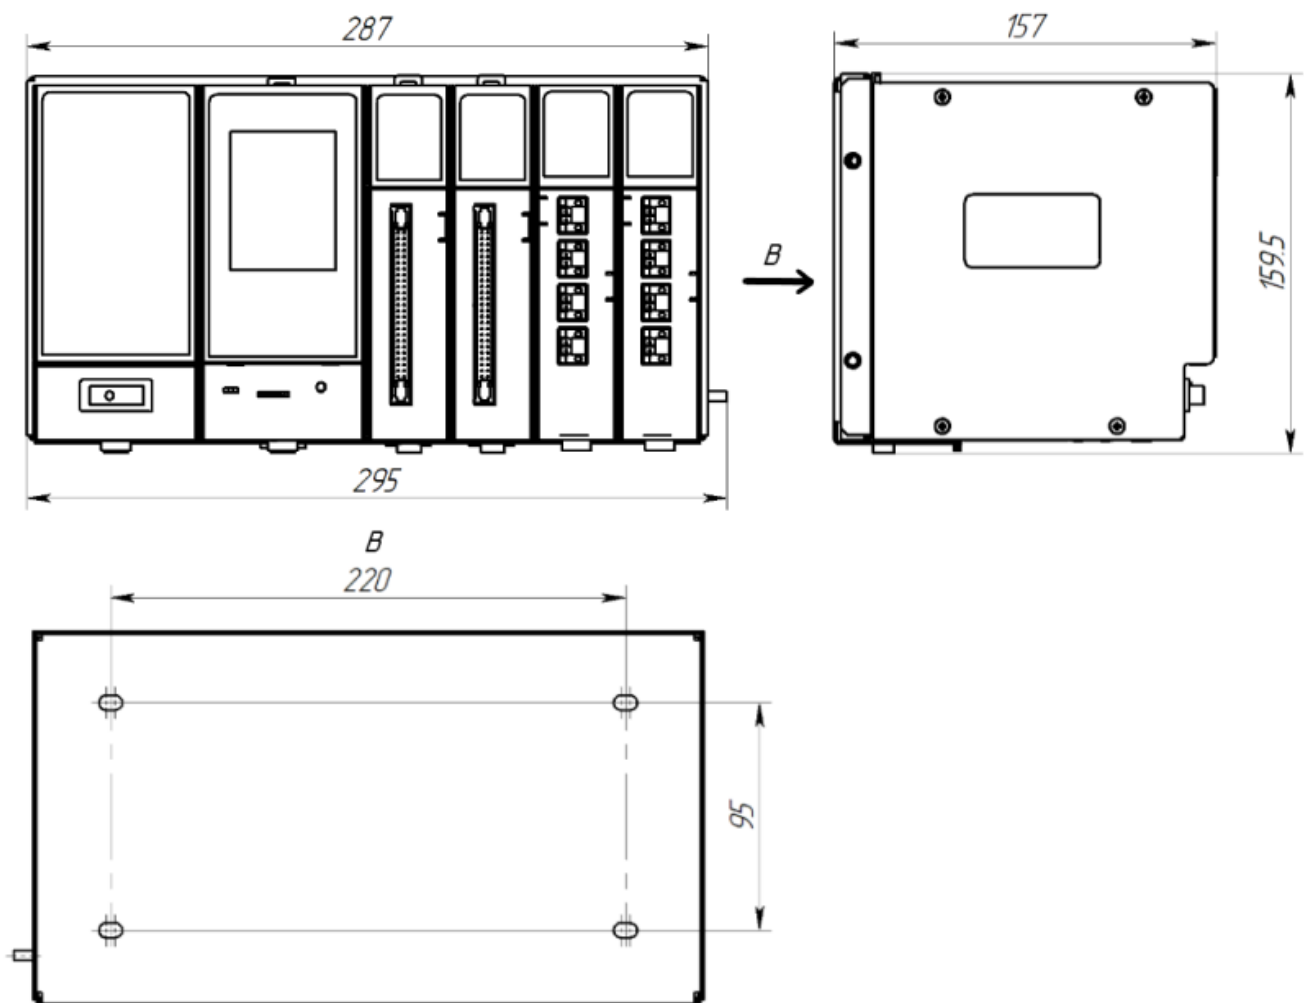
Габаритные и присоединительные размеры сборки контроллера на шасси SH-08 с модулями в металлическом корпусе
